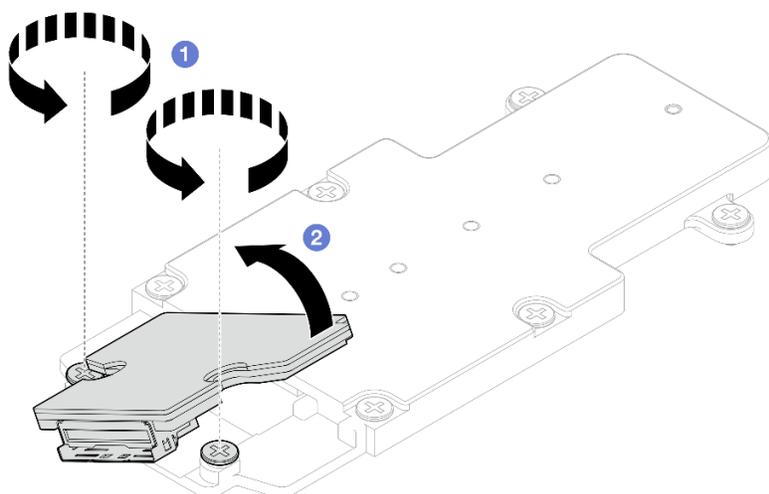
Desmontaje del conjunto de placas posteriores de M.2
